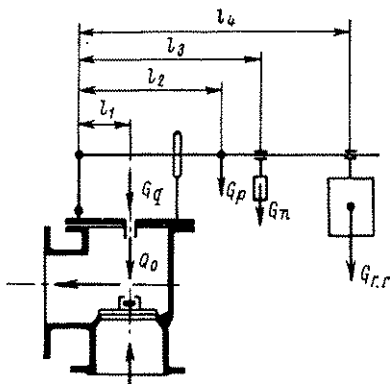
Схема рычажно-грузового малоподъемного предохранительного клапана
